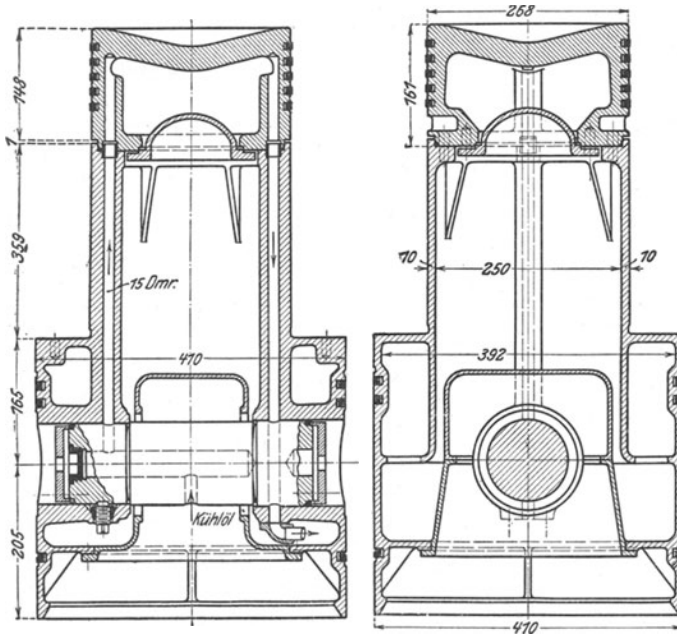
123. Gemeinsamer Arbeits- und Spülpumpenkolben.
